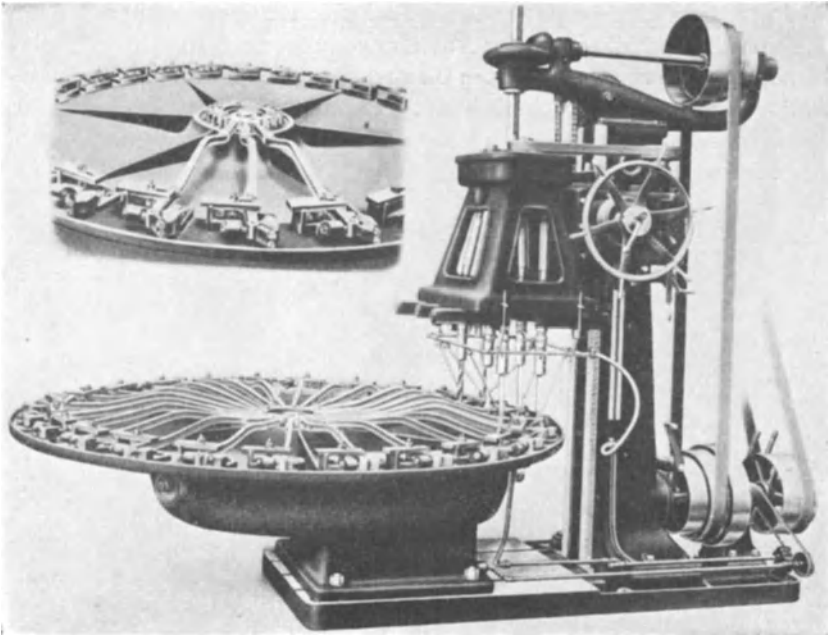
Phönix-Bohrmaschine mit Sonderbohrvorrichtung, teilbarer Vorschub. spindelbohrmaschinen zu einer sogenannten Bohrmaschinenstraße. Die Vorrichtung für die Aufnahme des Werkstückes wird in solchem
